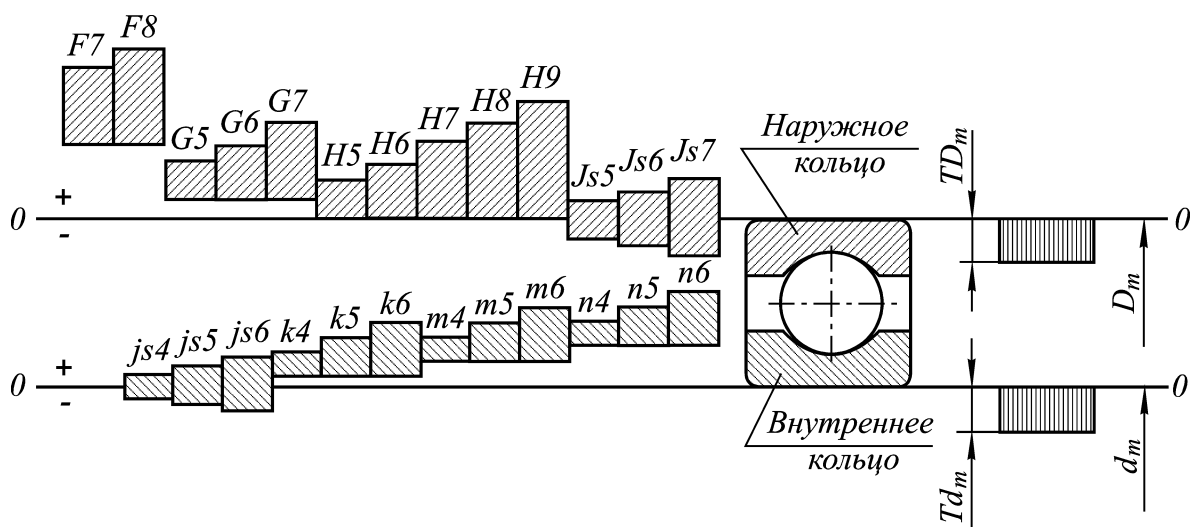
Схемы полей допусков посадок колец подшипников на вал и в корпус при вращении вала с внутренним кольцом подшипни-
